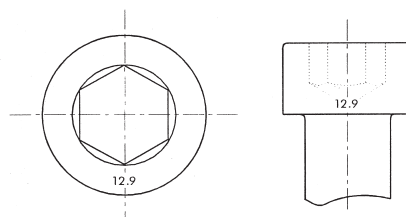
Abb. G: Beispiel für die Kennzeichnung von Zylinderschrauben mit Innensechskant
